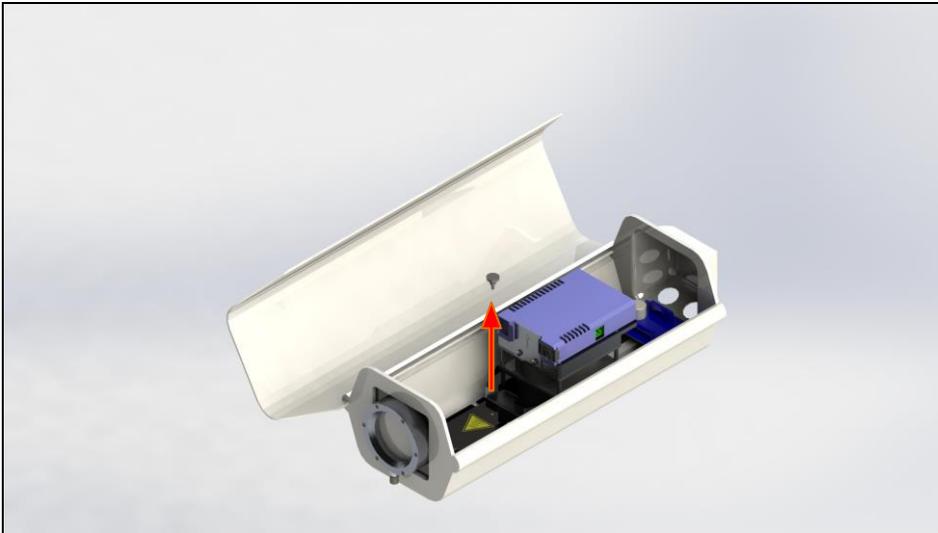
Lösen der Rändelschraube vom Befestigungsblech
